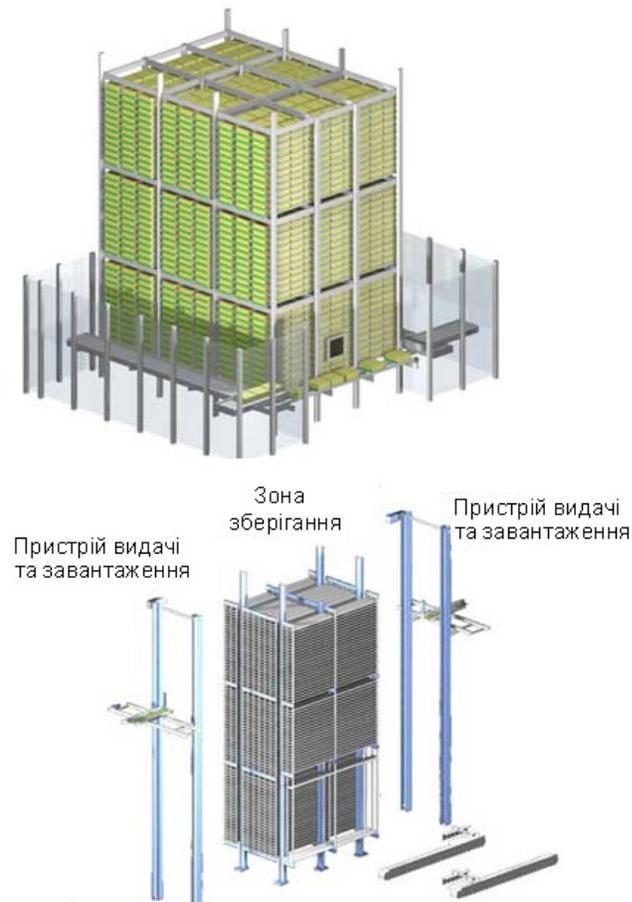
Схема автоматичного складу для зберігання коробок [80]
